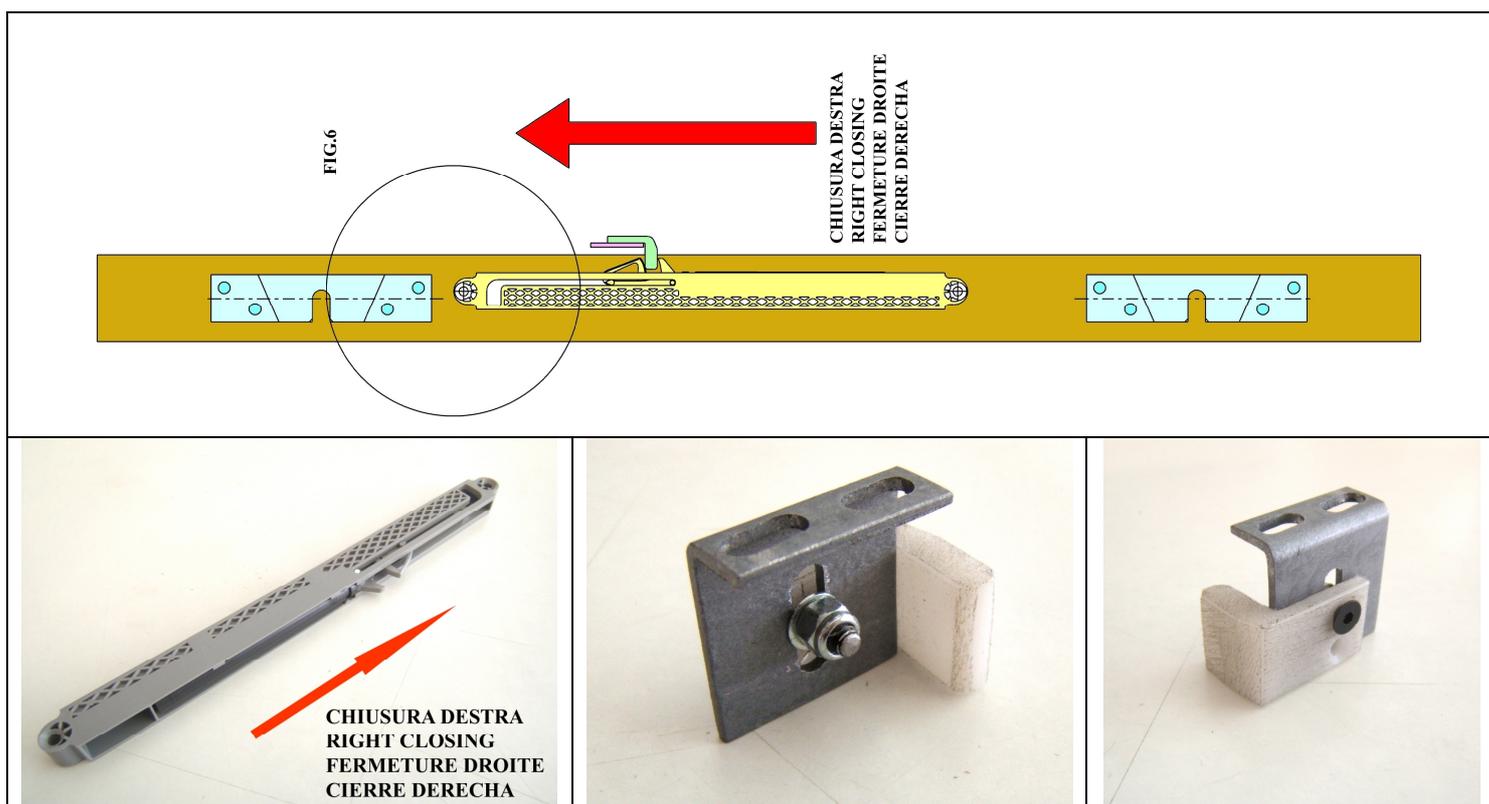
Montaggio dei particolari con chiusura a destra - Assembly instructions of the parts with right closing
